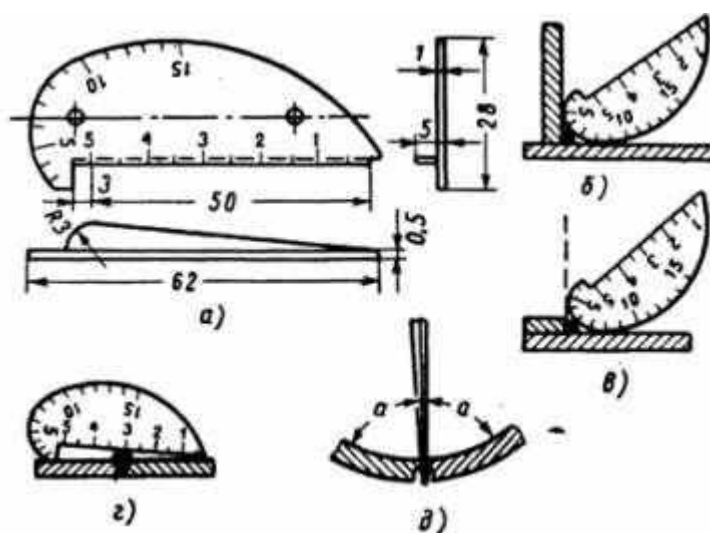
Универсальный шаблон А. И. Красовского для проверки формы и размеров швов: а – общий вид шаблона; б и в – измерение высоты углового шва; г – измерение высоты стыкового шва; д – измерение зазора
